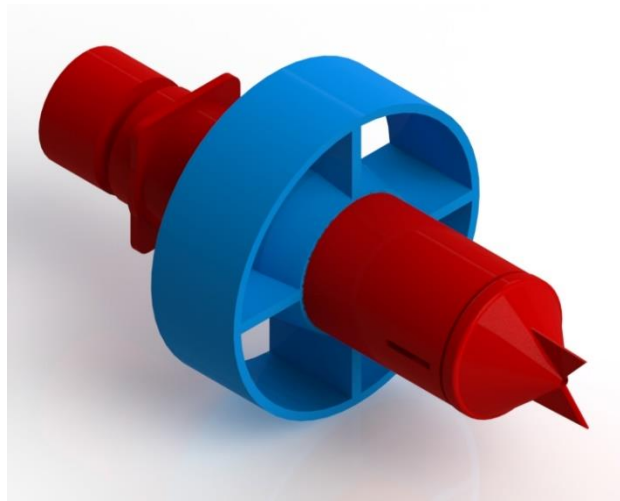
SPÜLDÜSE FÜR DIE VERPACKUNG
